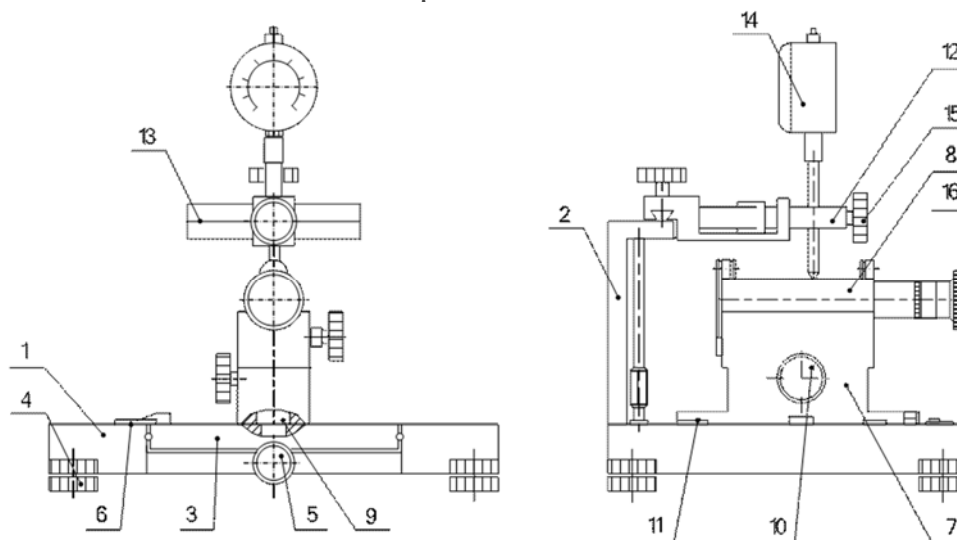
Устройство установки МЛИ-1М. 1 – основание; 2 – стойка; 3 – стол измерительный; 4 – регулируемые ножки; 5 – винт; 6 – шкалы; 7 – устройство базирования; 8 – измеряемый образец; 9 – стержень переходной; 10 – винт; 11 – упор; 12 – кронштейн; 13 – устройство коррекции; 14 – индикатор; 15 – юстировочный винт; 16 – съемная рукоятка.
